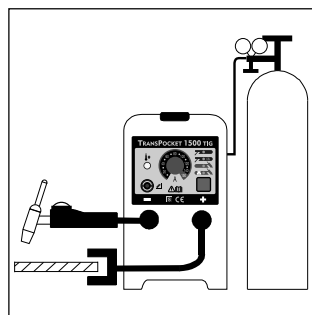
TP 1500 TIG equipado com o queimador de soldadura AL 1500
